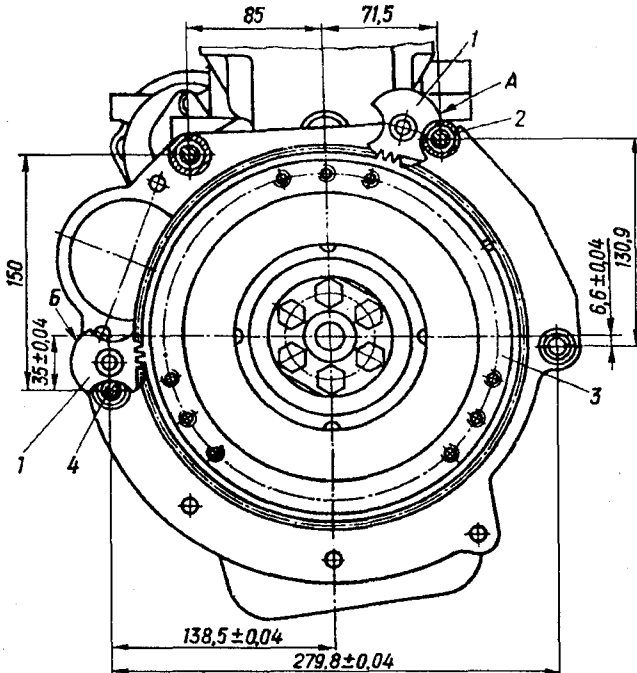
Стопоре маховика при разборке и сборке: 1 – стопор маховика зубчатый; 2 – втулка приспособления для крепления двигателя при разборке и сборке; 3 – маховик; 4 – болт; А – стопорение маховика при установке двигателя на приспособление; Б – стопорение маховика (двигатель на приспособление не установлен)
